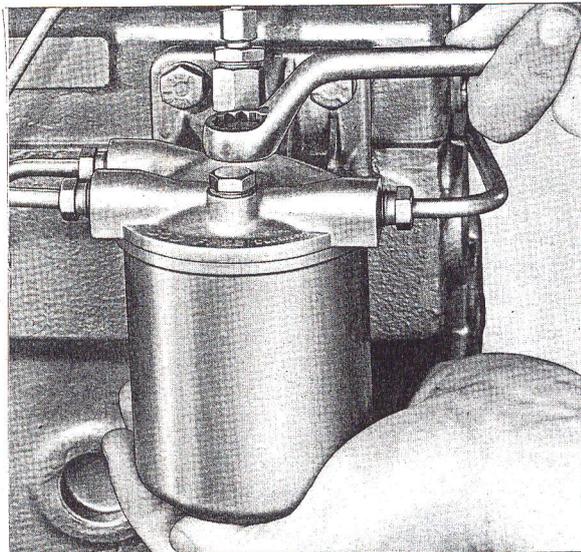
Dépose de la vis d'assemblage de la cuve du filtre.
